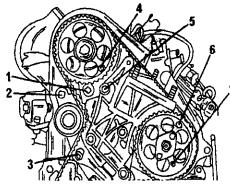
Передняя сторона двигателя с подробностями для снятия зубчатого ремня.
